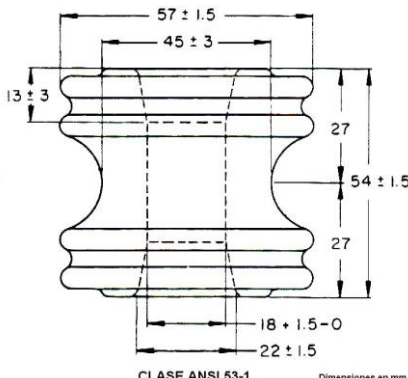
Especificaciones generales para Aislador tipo Carrete 53- 1 AB
